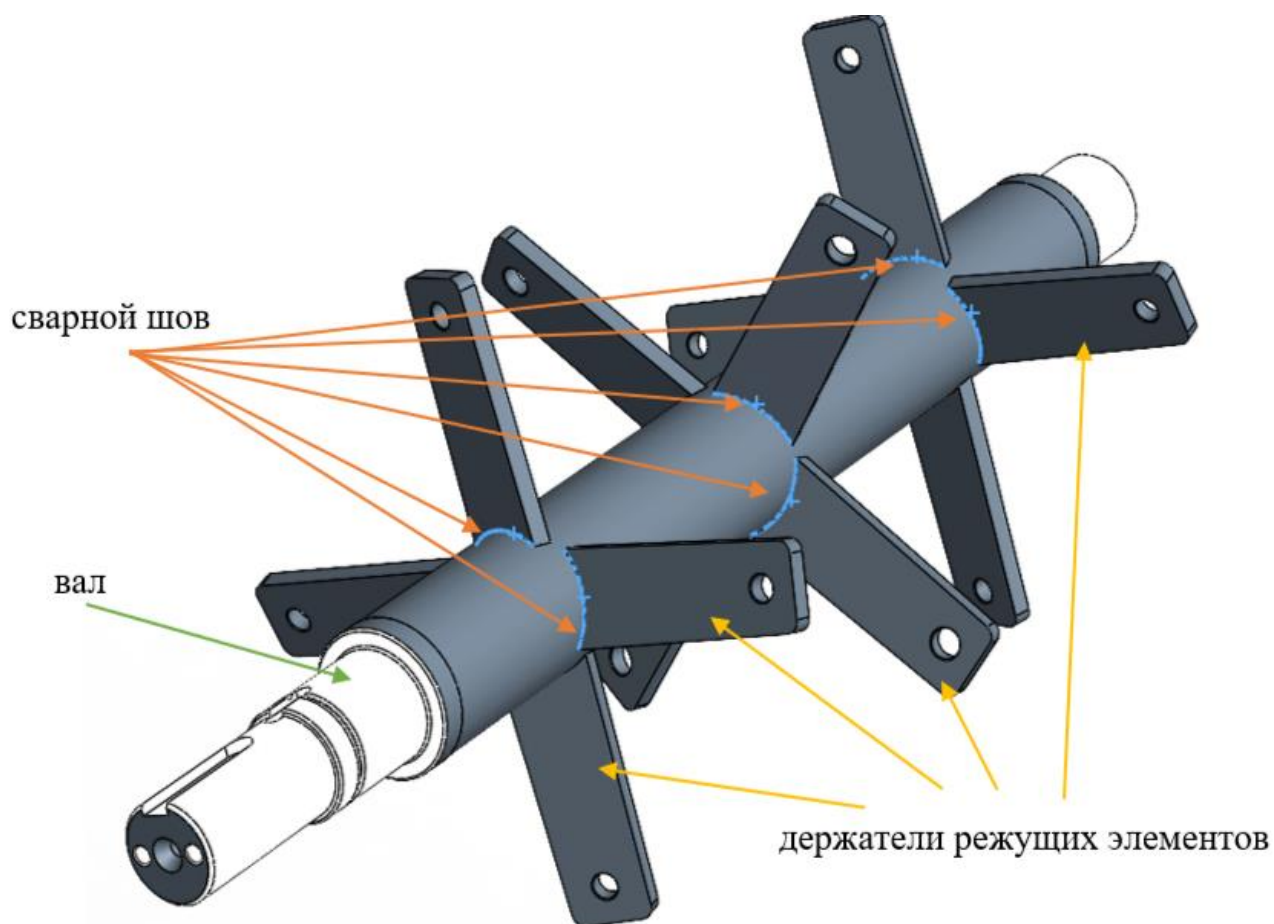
3D модель вала установки с указанием зон сварного шва
